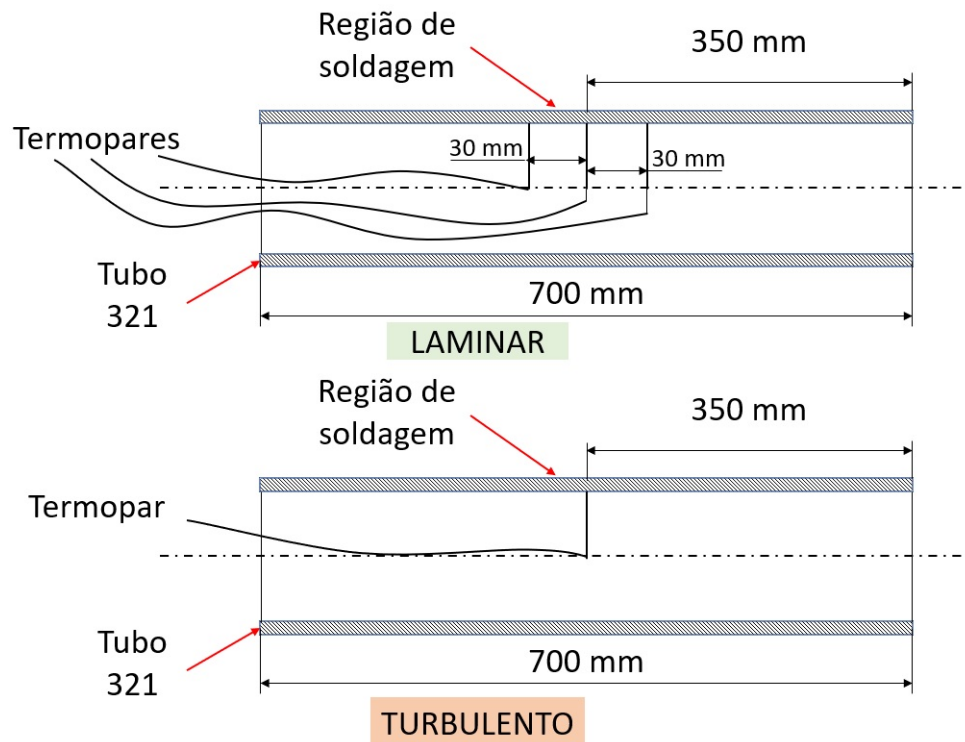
Posicionamento dos termopares soldagem AISI 321
